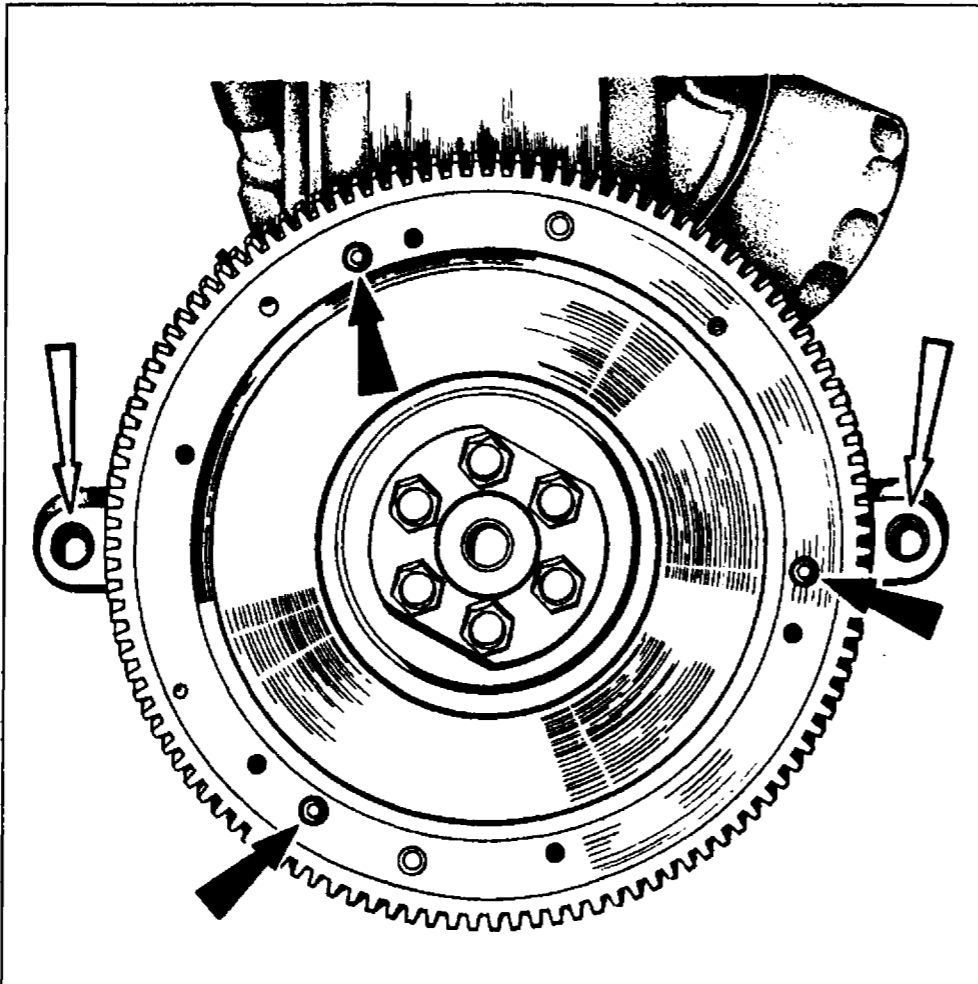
Установочные штифты сцепления (черные стрелки) и центрирующие втулки коробки передач (белые стрелки)
